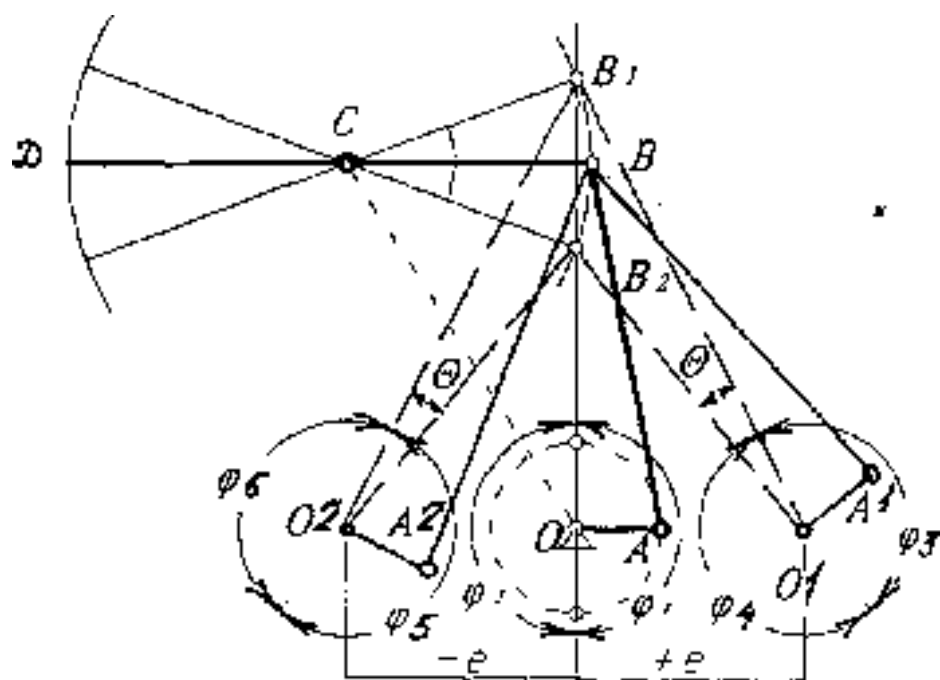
Преобразующий механизм обычных станков-качалок для трех случаев расположения кривошипного центра
